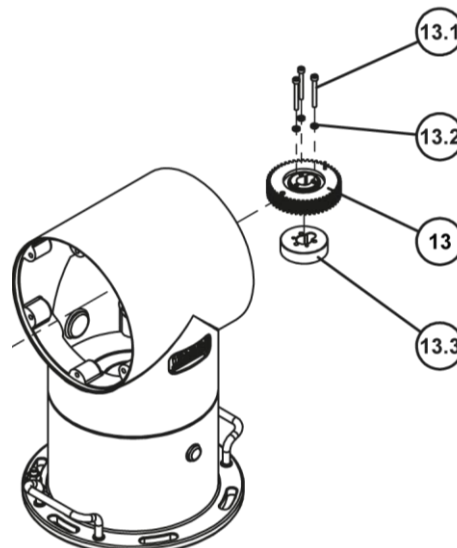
Explosionszeichnung Schwenk-Neigeeinheit mit Scissor gear pan
